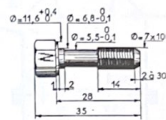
Tornillo racor MR-3705 para la conexión del manómetro en la prueba de la presión de aceite. Se monta en la culata izquierda, retirando antes el tornillo racor del tubo de engrase.
